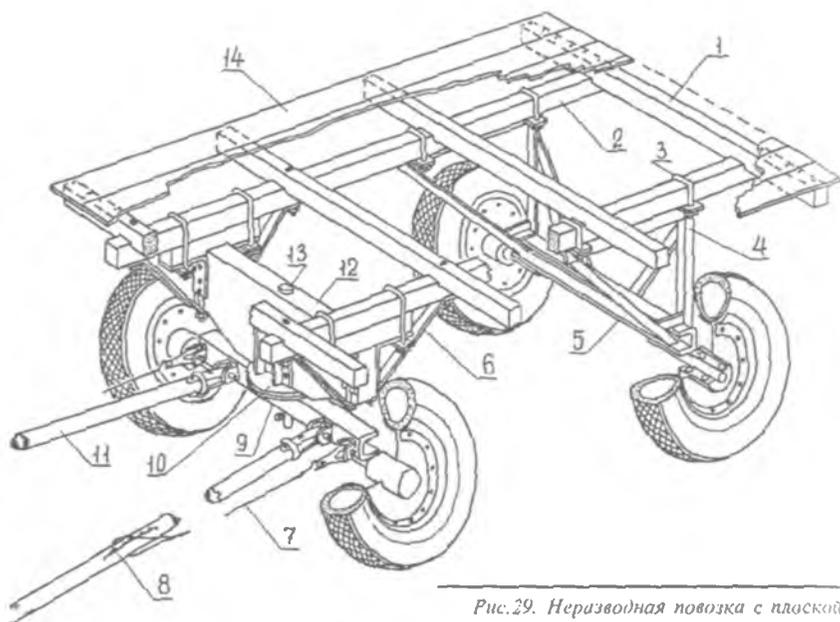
Неразводная повозка с плоской платформой на резиновом ходу
